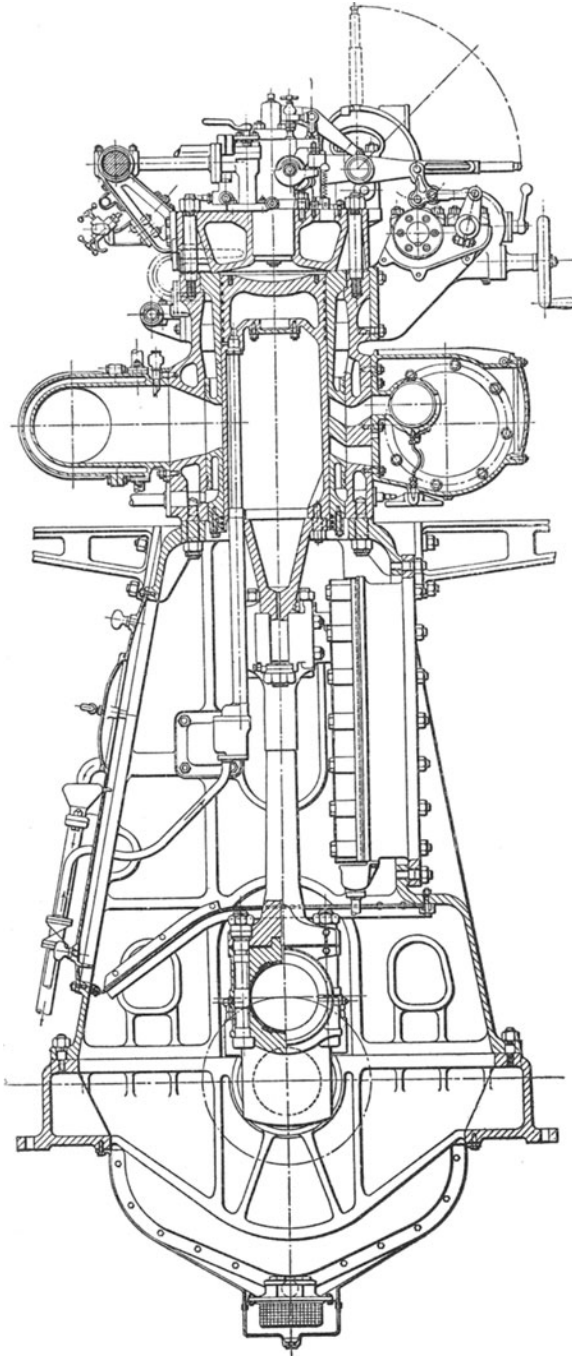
Zylinderschnitt der Stephen-Sulzer-Maschine.
